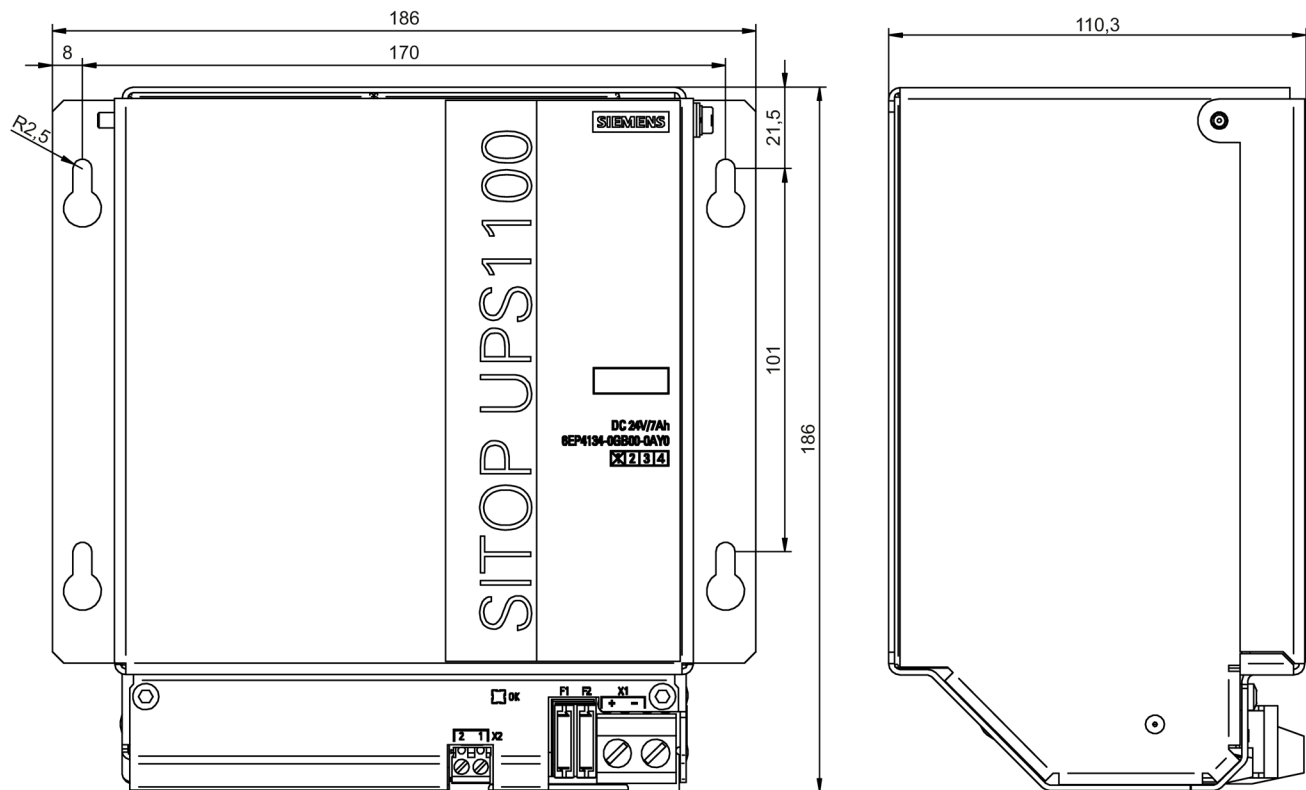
Maßzeichnung 6EP4134-0GB00-0AY0
